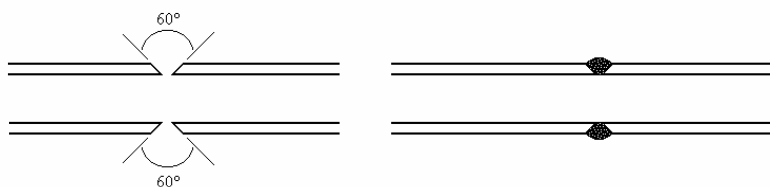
9 Soldadura en tubería de acero espiga espiga.
